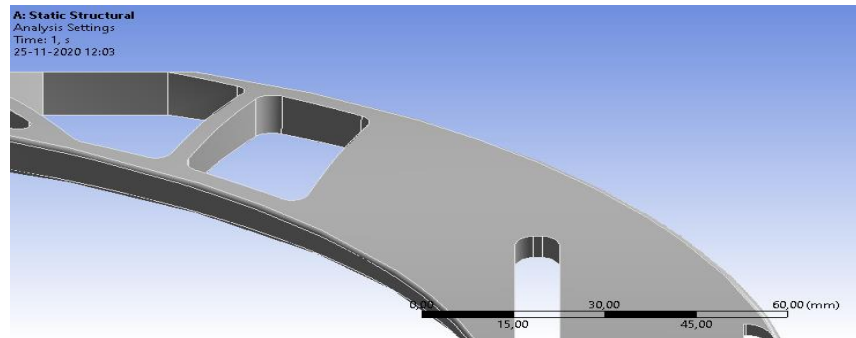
Vista 2 rediseño N°4 de eslabón pierna izquierda.
